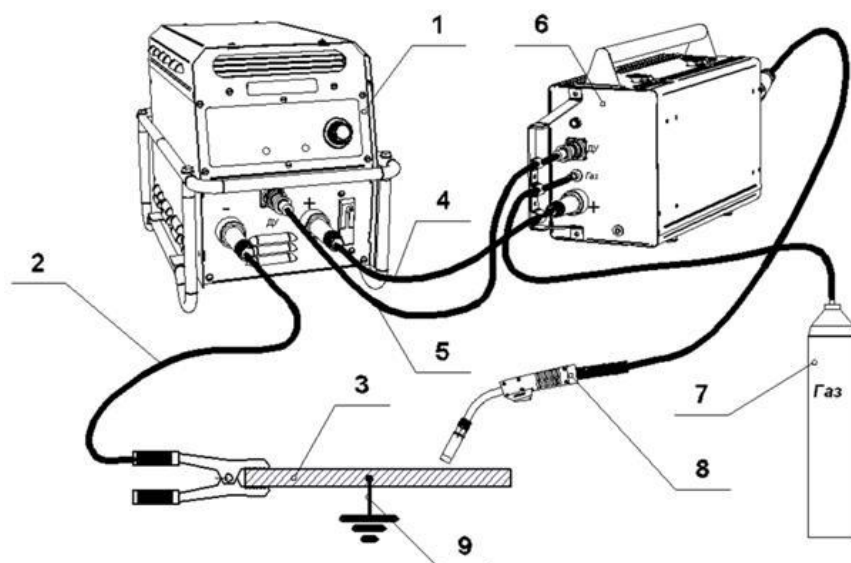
Схема сварочного полуавтомата:
